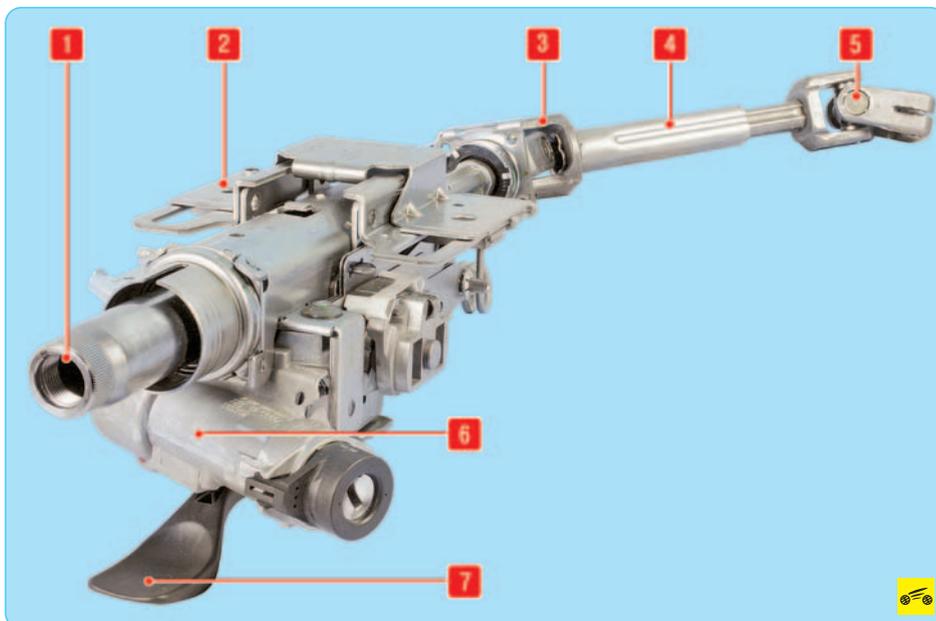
Рулевая колонка: 1 – рулевой вал; 2 – кронштейн крепления рулевой колонки; 3 – верхний карданный шарнир промежуточного вала; 4 – промежуточный вал; 5 – нижний карданный шарнир промежуточного вала; 6 – выключатель (замок) зажигания; 7 – рычаг механизма регулировки положения рулевой колонки
